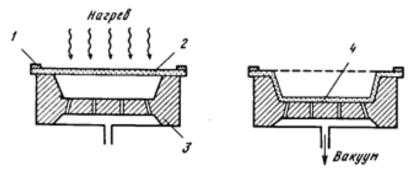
Схема процесса вакуумформования изделия из термопластичной листовой заготовки [19]
